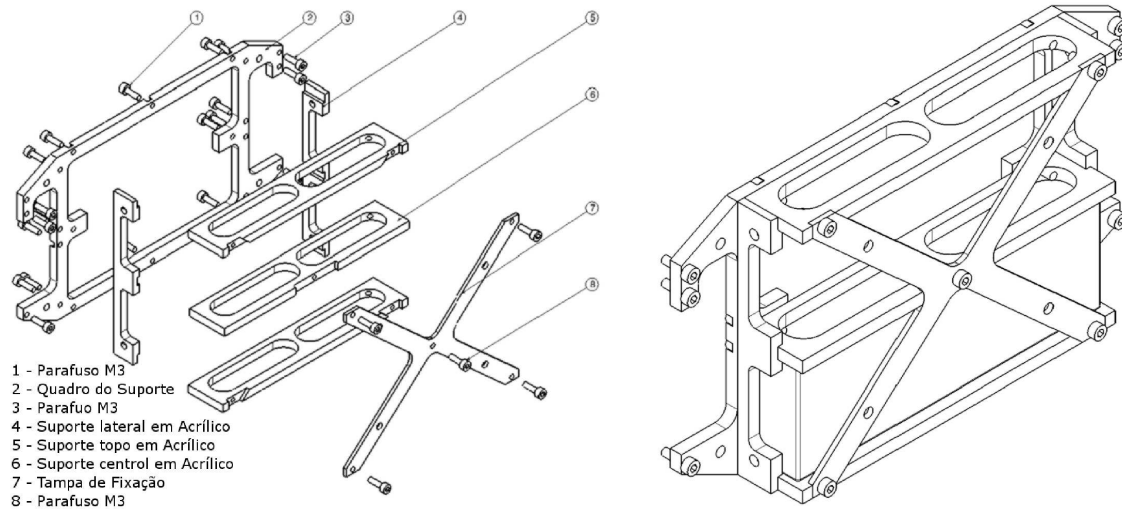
Vista explodida e de conjunto do módulo das baterias
